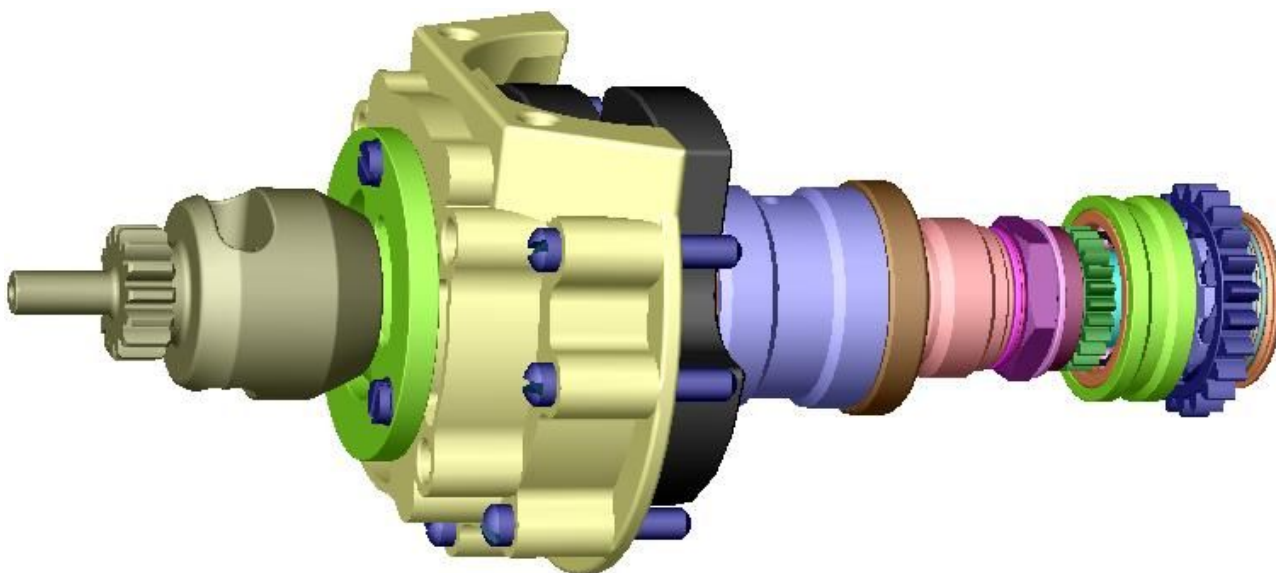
Сборка среднего уровня «Группа вала» двигателя Д300
